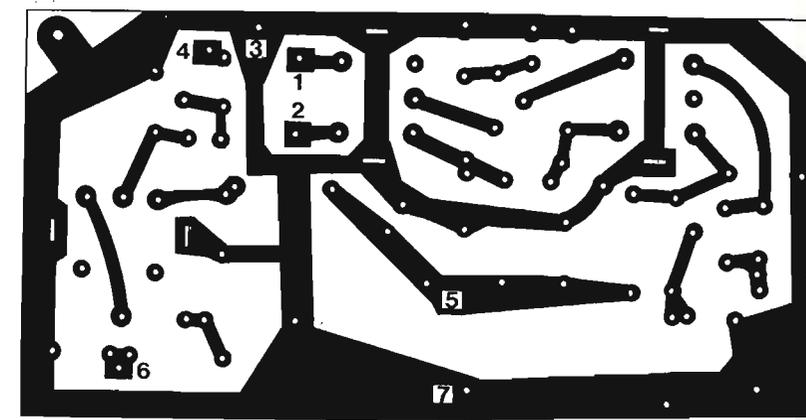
Il lavoro di montaggio del dispositivo di misura delle induttanze deve essere iniziato con la costruzione del circuito stampato di cui appare qui il disegno in scala 1/1.
